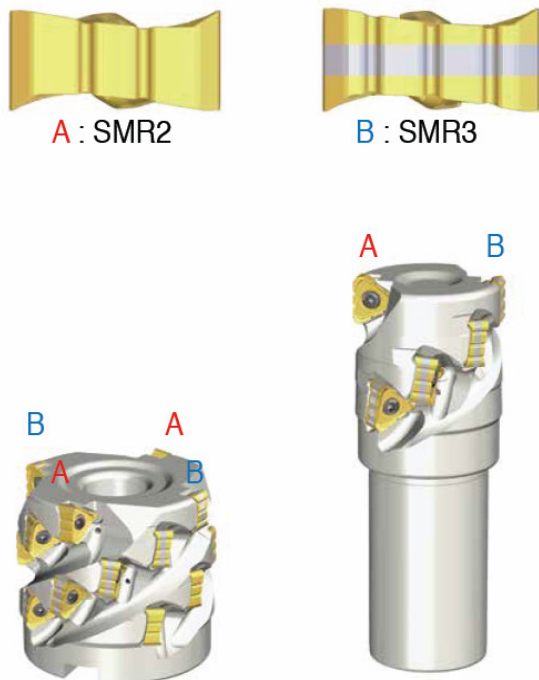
Схема крепления пластин с двумя и тремя насечками
